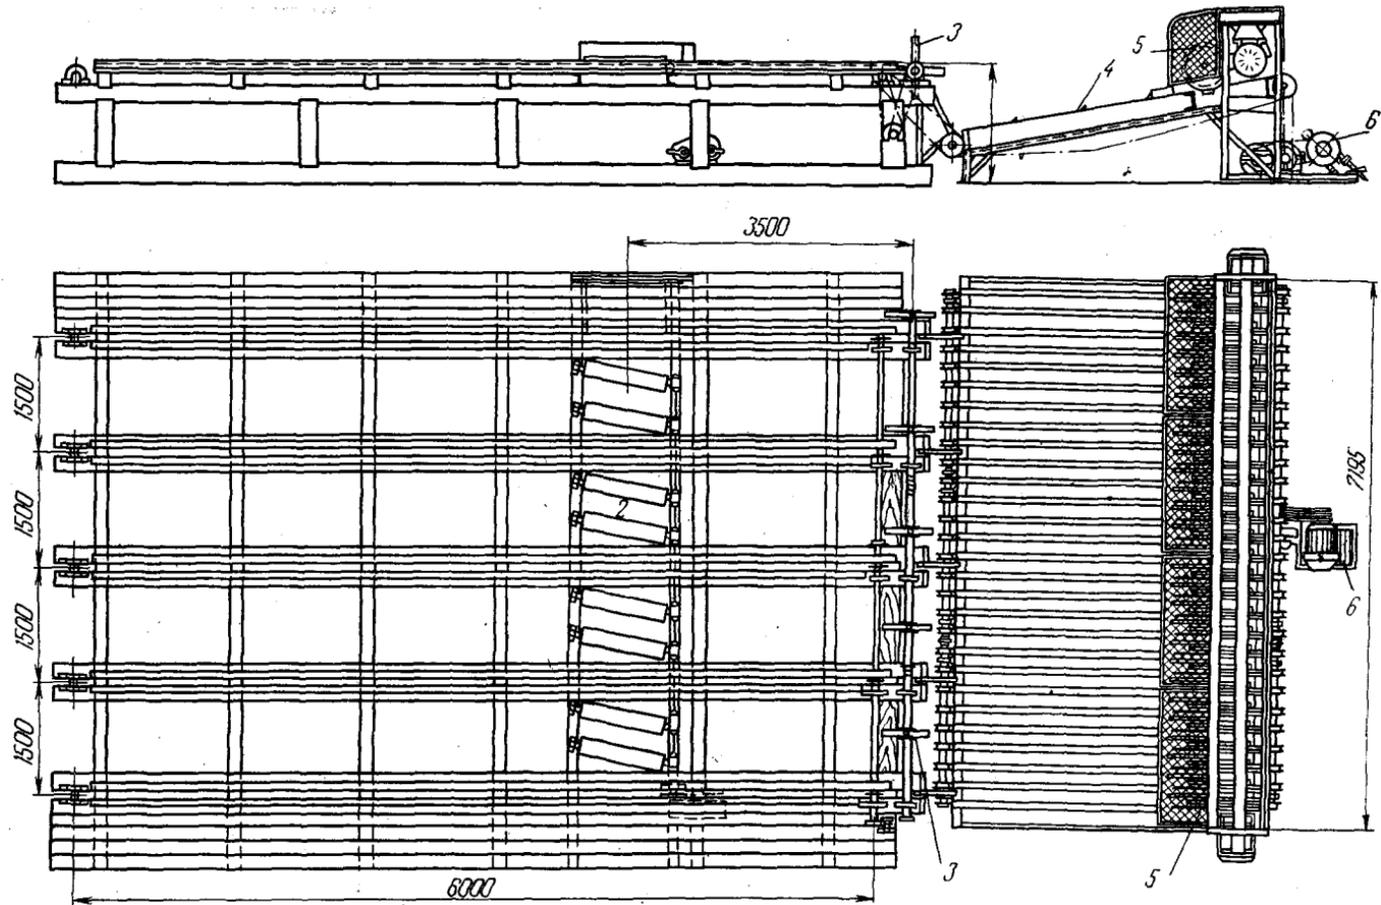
Торцовочный 27-пильный агрегат (триммер):
